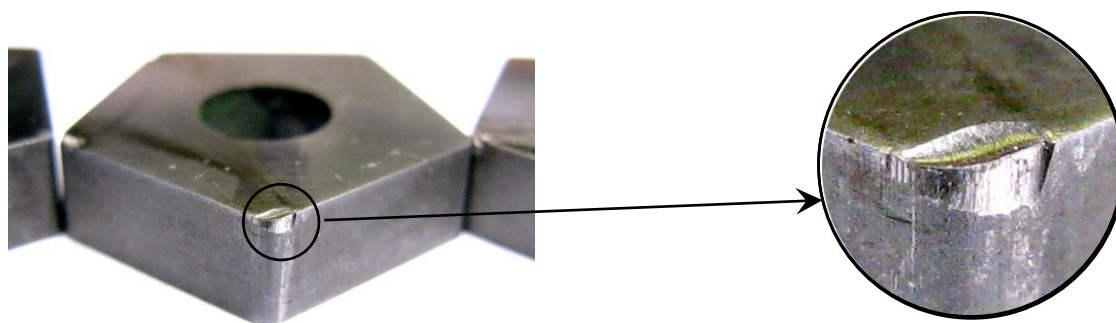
Типичная картина износа твердосплавных пластин из твердого сплава ВК8 при фрезеровании стали 45
